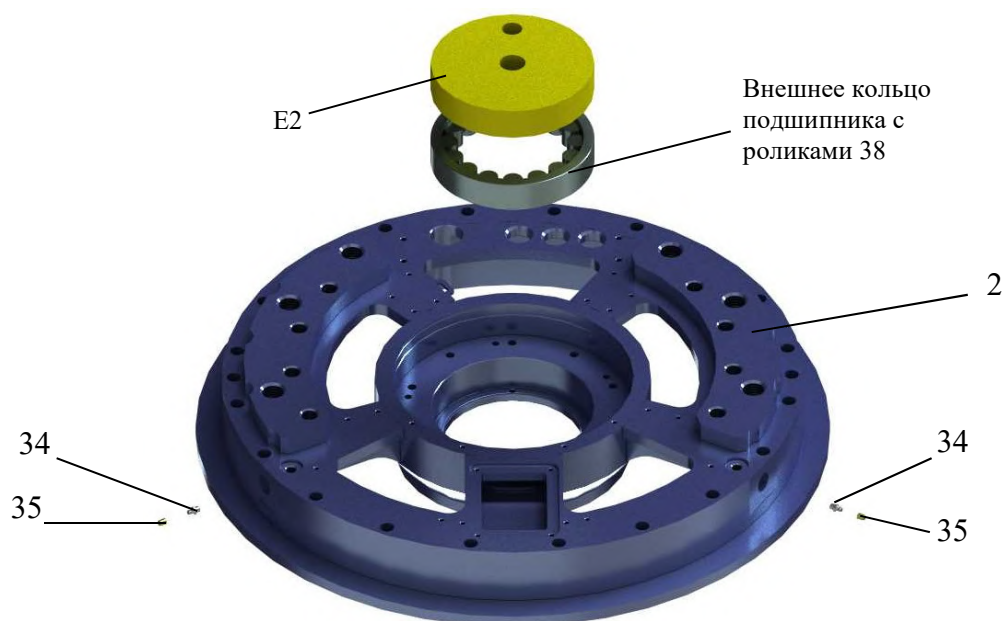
Установка роликового подшипника в подшипниковый щит со стороны тормоза
